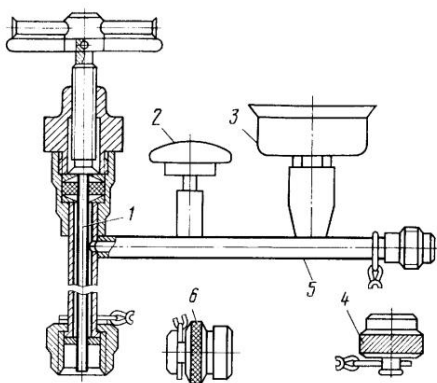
Приспособление для проверки давления и зарядки амортизатора шасси:
